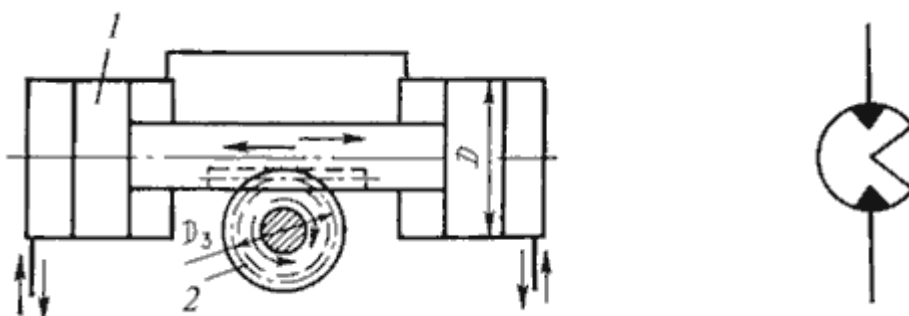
Речно-шестеренный механизм; 2.20 - Условное обозначение поворотного гидроцилиндра
